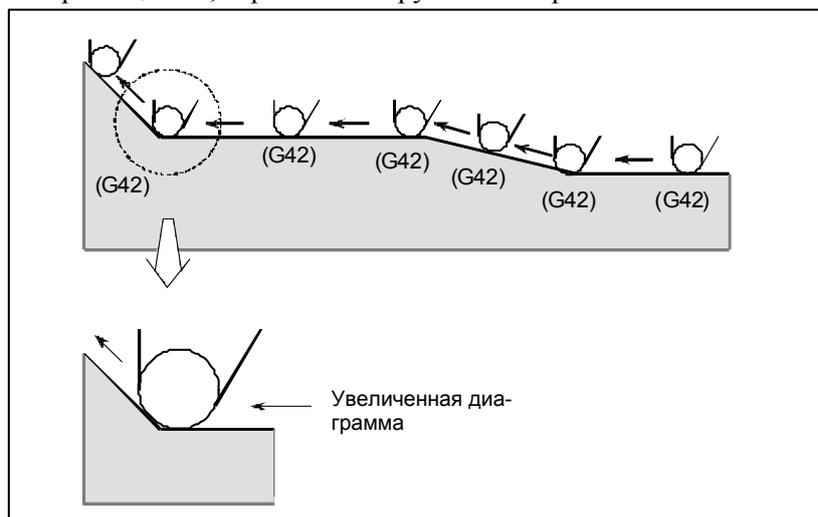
(c) Перемещение инструмента, при котором положение заготовки не меняется
